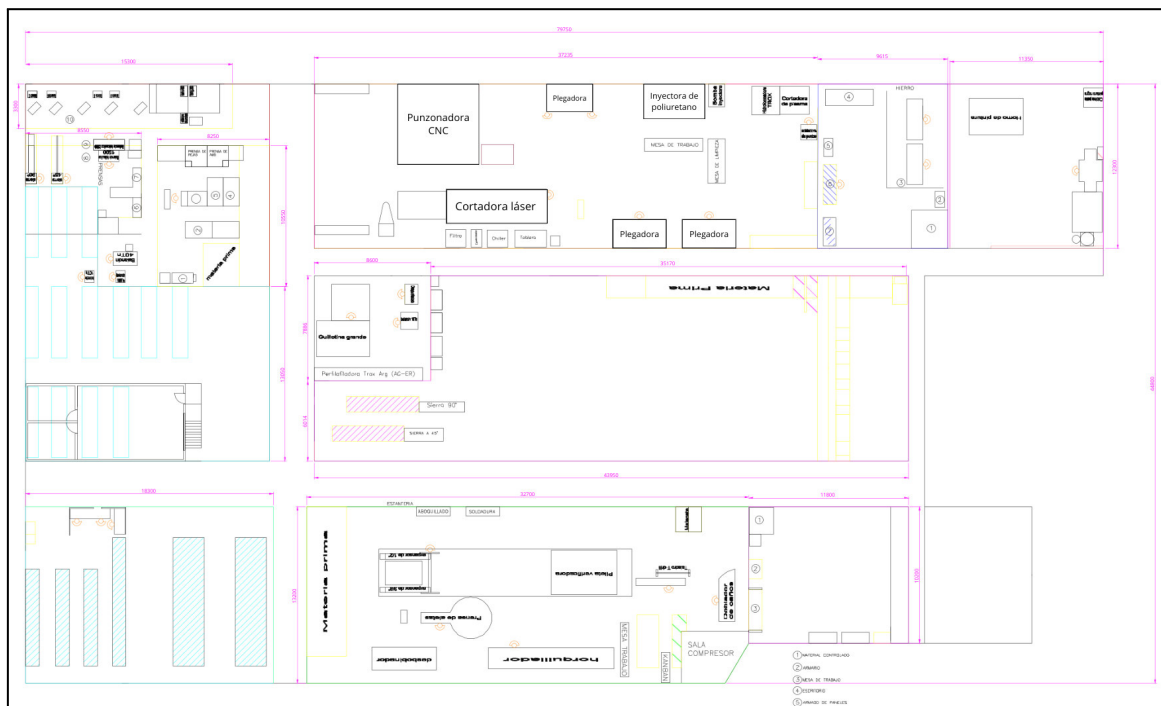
Layout completo de la planta. El sector de chapistería se ubica en la zona central superior.
